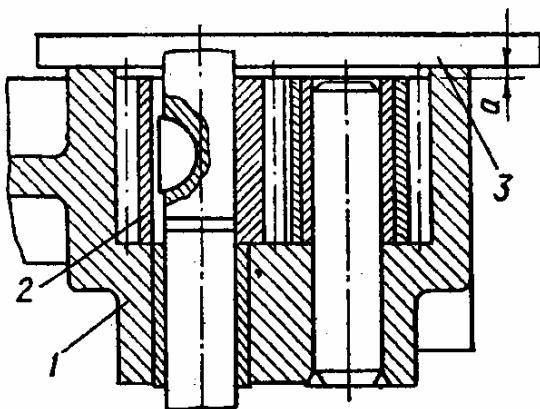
Перевірка торцевих зазорів між шестернями і корпусом масляного насоса:
